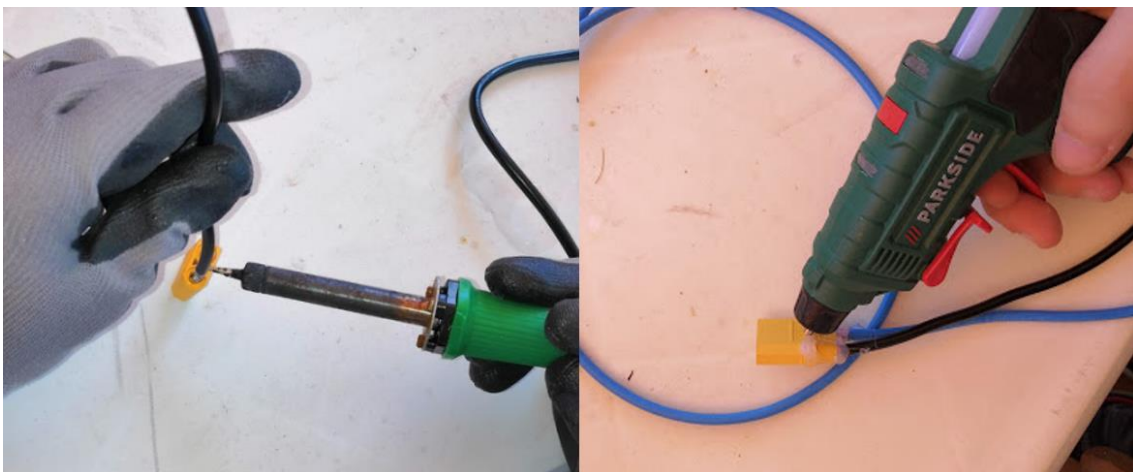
Soldadura de terminales y recubrimiento con silicona
